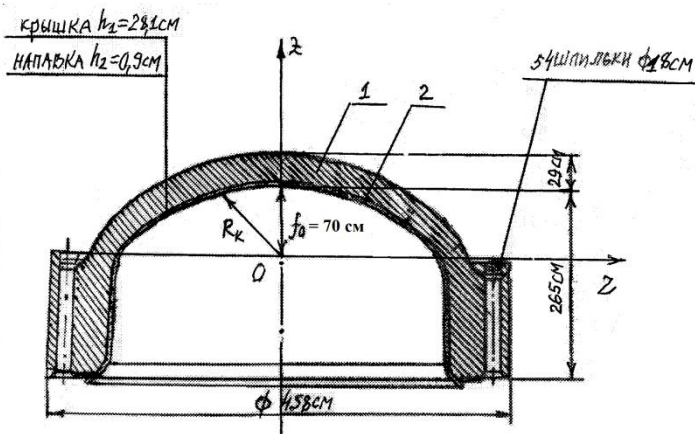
Крышка ядерного реактора: 1 – материал основного металла  $h_1 = 28,1$  см;
